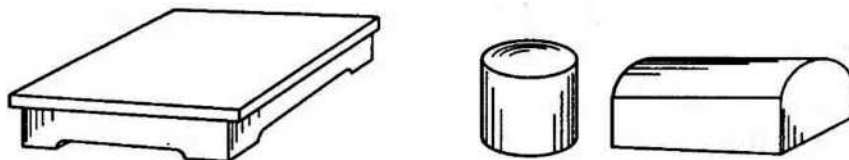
Общий вид правильной плиты с рихтовальными бабками
